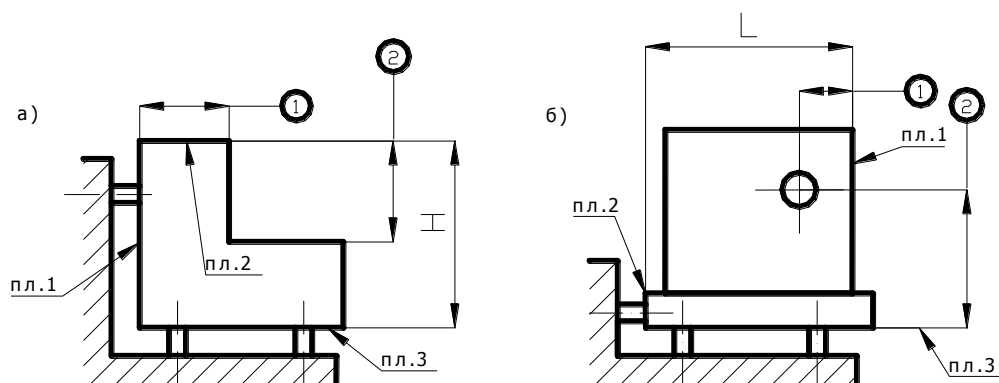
Базирование заготовки при фрезеровании углового паза (а) и сверлении отверстия (б).
